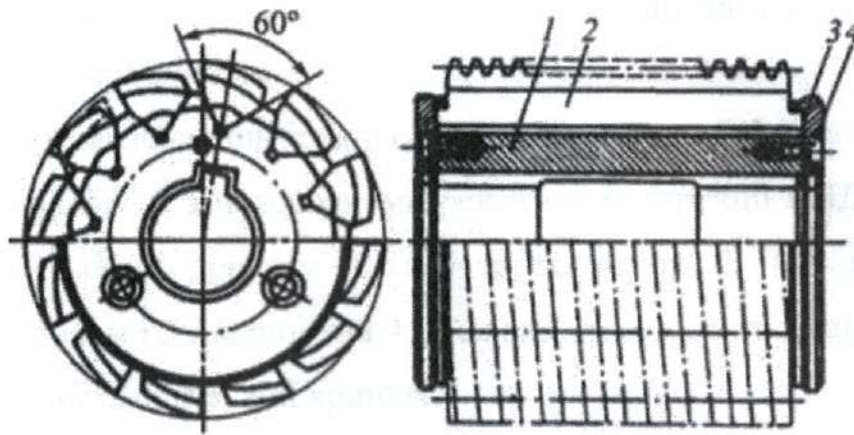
Збірна черв'ячна фреза з поворотними рейками фірми «Сампутенсілі»
